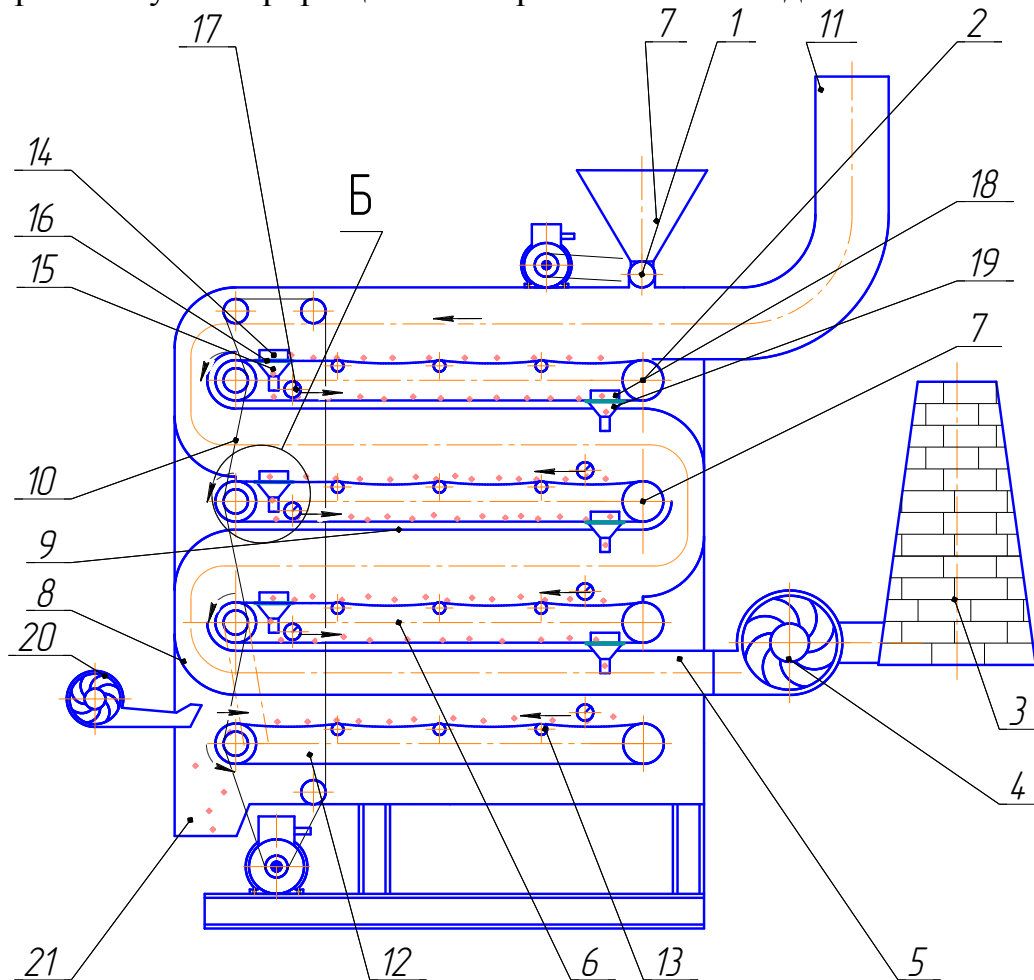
Конвейерная установка для сушки пророщенного зерна. 1 - шнек; 2, 6, 7, 12 - перфорированный транспортер; 3 - труба котельной установки; 4 - вентилятор; 5, 9, 10 - воздуховод; 8 - направляющий щиток; 11 - вытяжной зонт; 12 - форсунка; 13 - встряхиватель; 14, 18 - сбрасыватель; 15, 19 - воронка; 16 - поддерживатель; 17 - шнек разравнивающий; 19 - лампы облучения; 20 - центробежный вентилятор; 21 - выгрузной патрубок.
